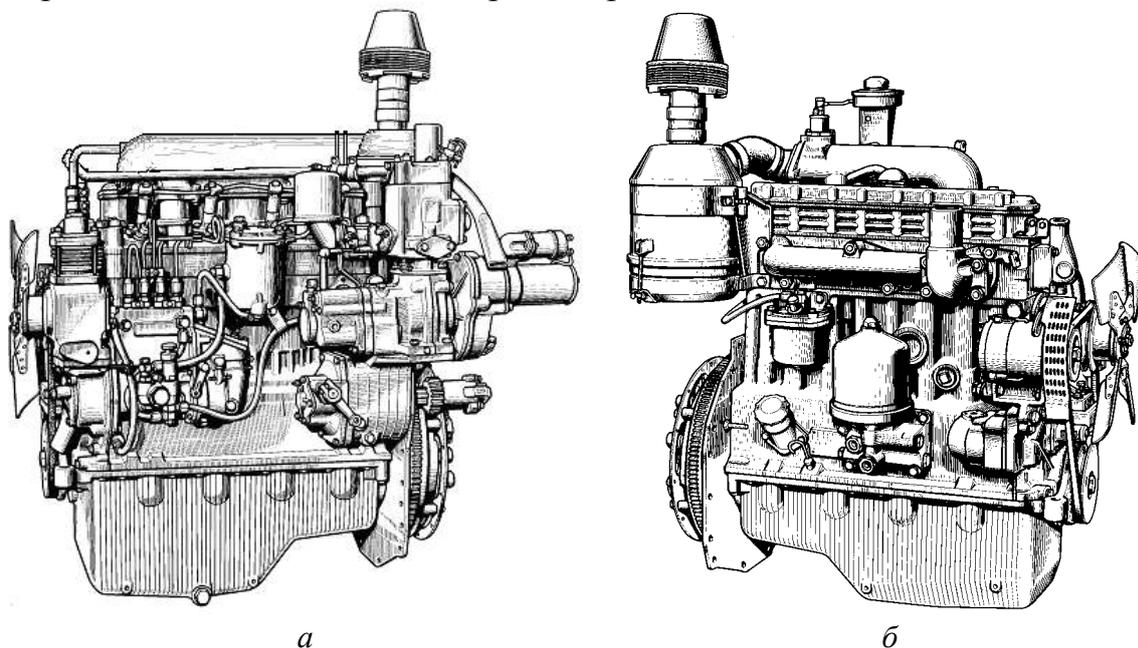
Общий вид дизеля Д-243 с муфтой сцепления, вентилятором, воздухоочистителем и пусковым двигателем: *а* – вид слева; *б* – вид справа
